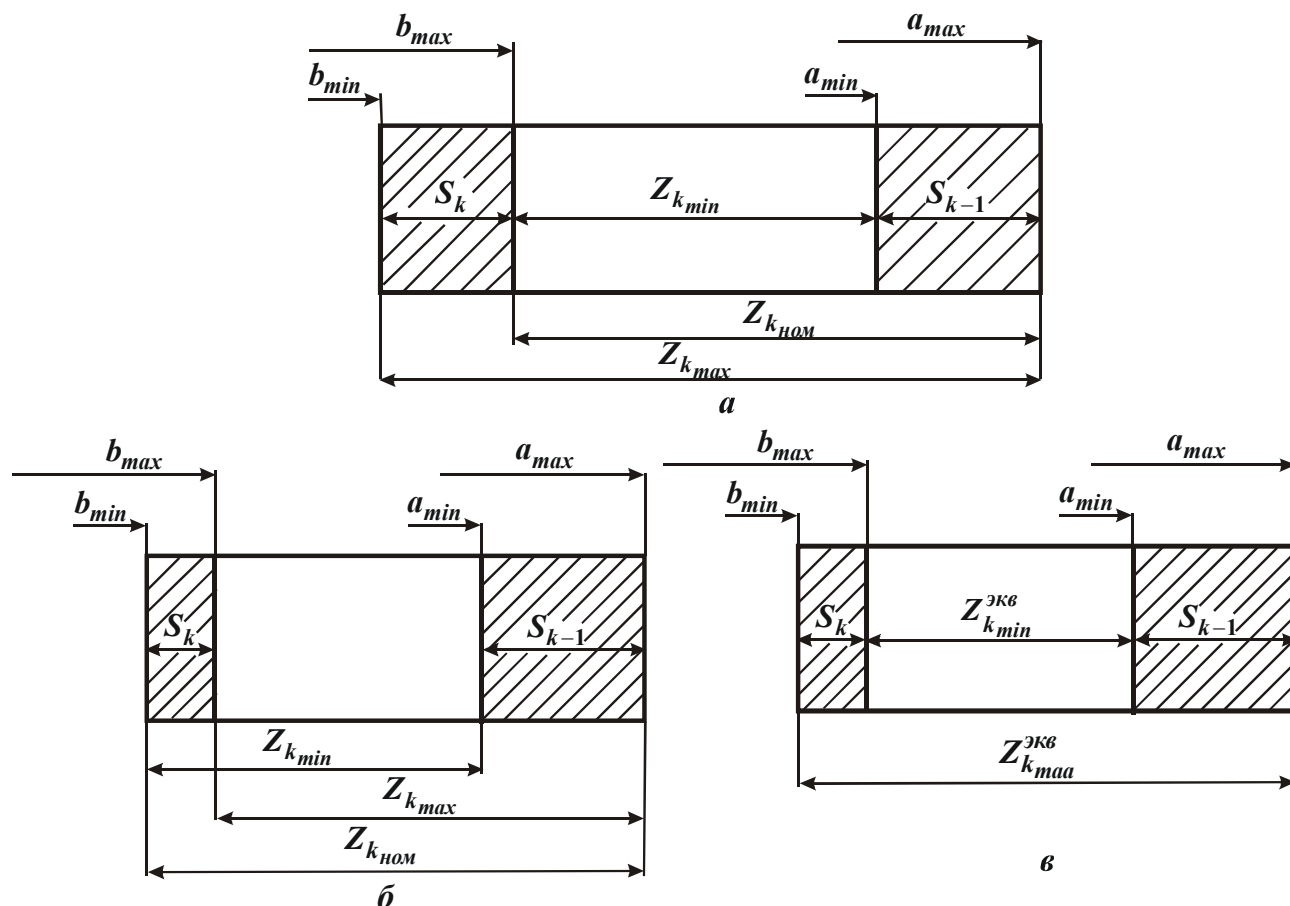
Схемы расположения припусков и допусков: для МППП (а), МАПР (б) и эквивалентная схема (в).
